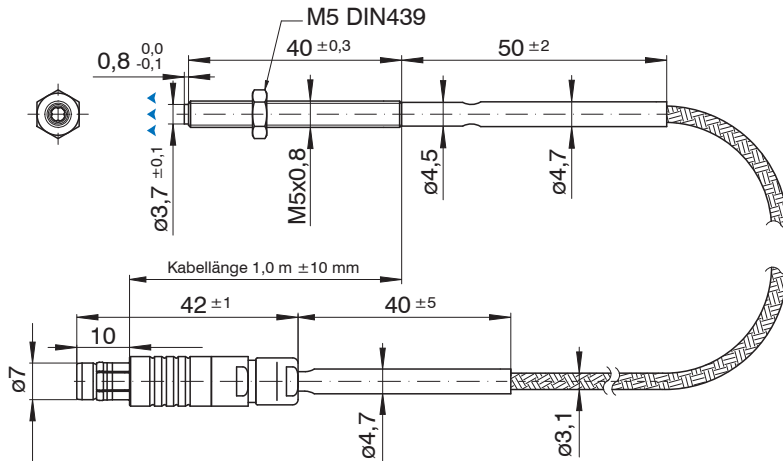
Sensor CSE025 mit integriertem Kabel mit Thermoschutzschlauch
